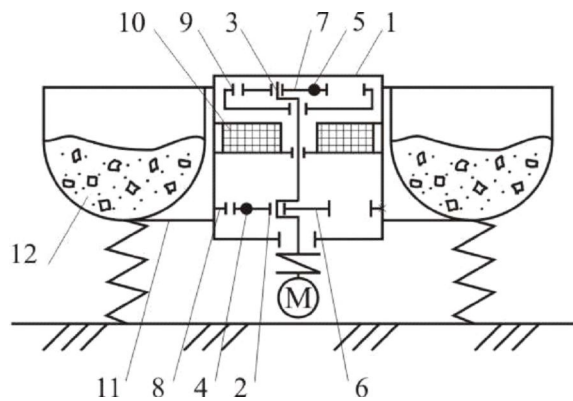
Вібраційно-відцентрова установка з регульованим вібратором: 1 - корпус, 2 – підшипник, 3 - колінчастий вал, 4 і 5 - дебаланси, 6 і 7 - зубчасті колеса, 8 і 9 - зубчасті вінці, 10 - електромагнітна муфта, 11 - віброплатформа, 12 - робоча камера
